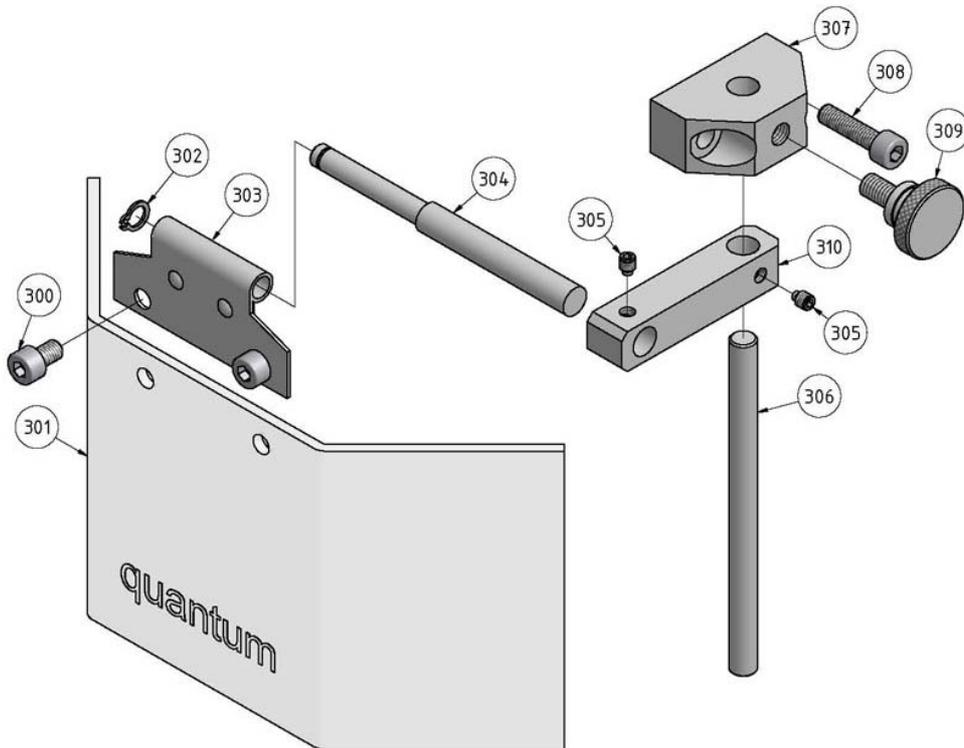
Fräsfutterschutz - Milling chuck protection
